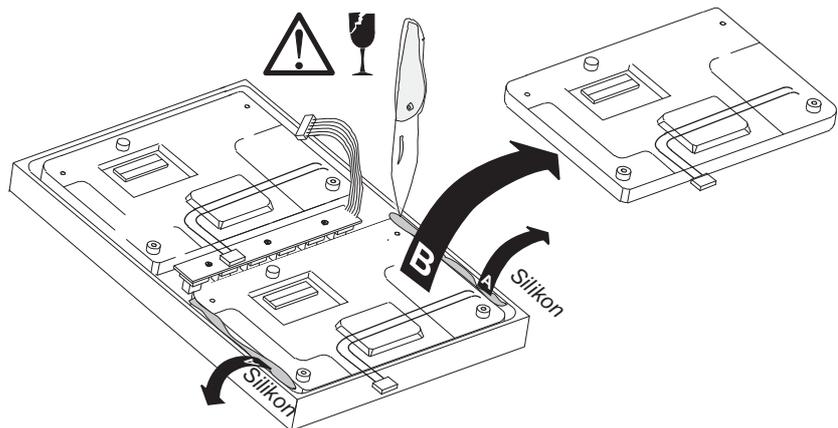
Lösen und Entfernen des defekten Displays
